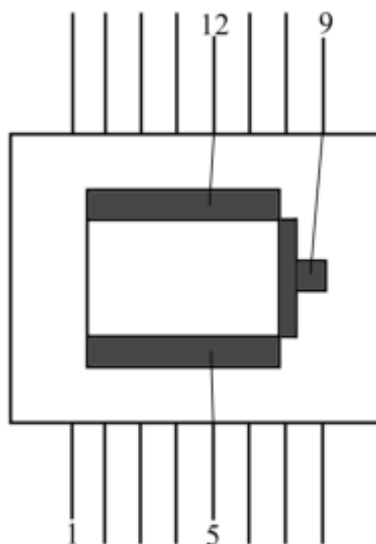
Схема разварки изделия в корпус держателя для микросхем
